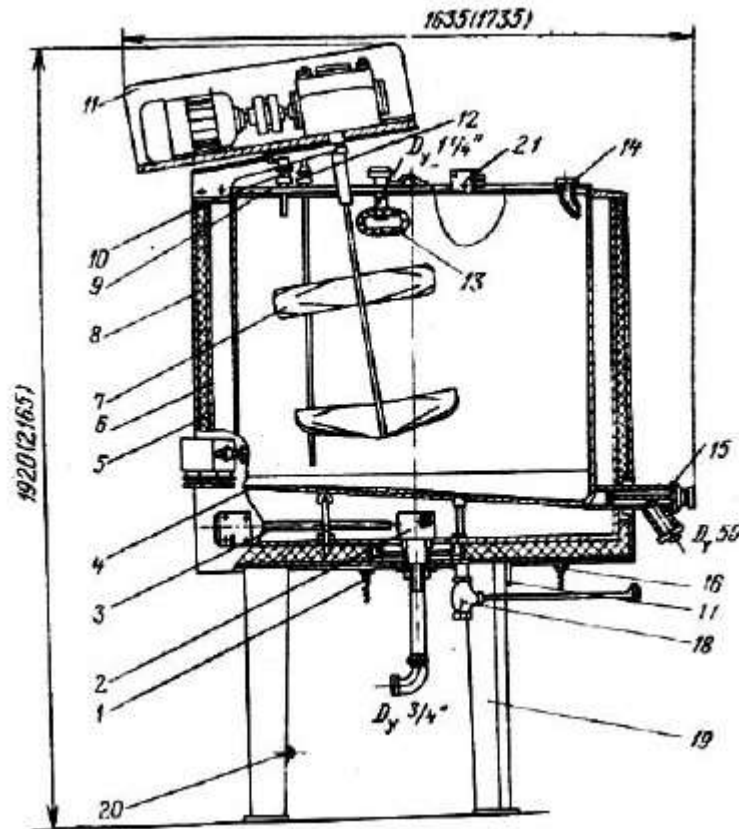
Общий вид установки заквасочной ОЗУ-600:
